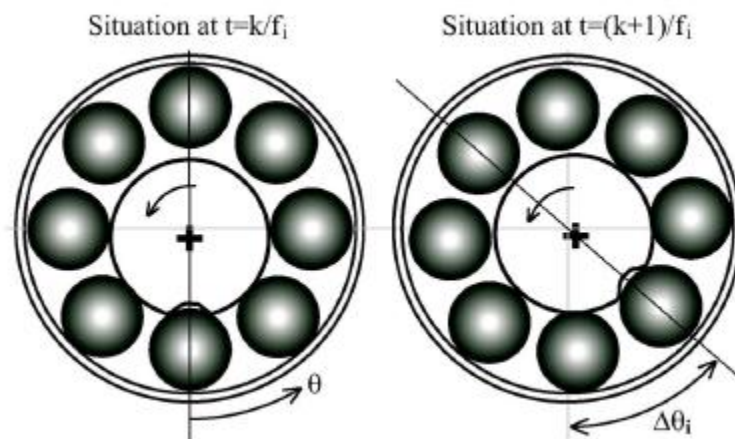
Movimento radiale del rotore dovuto ad un difetto sulla pista interna [21].
